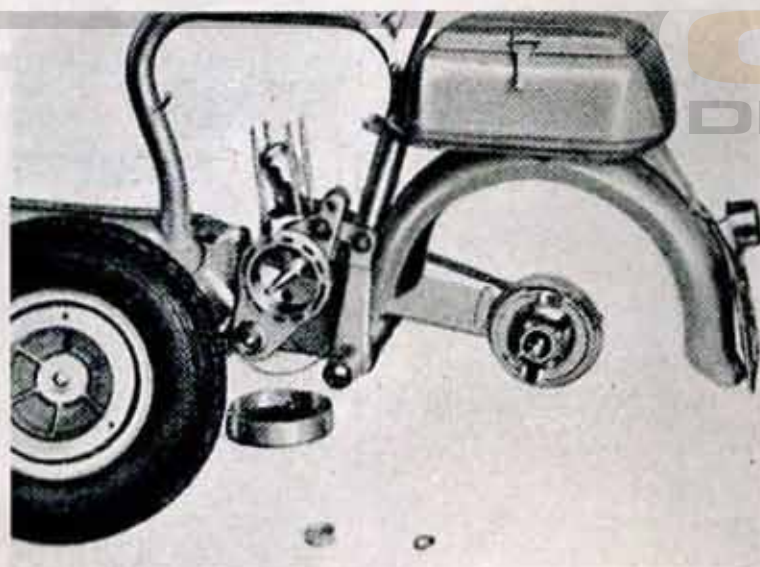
Démontage du pneu et des sections de la jante de la roue arrière.
